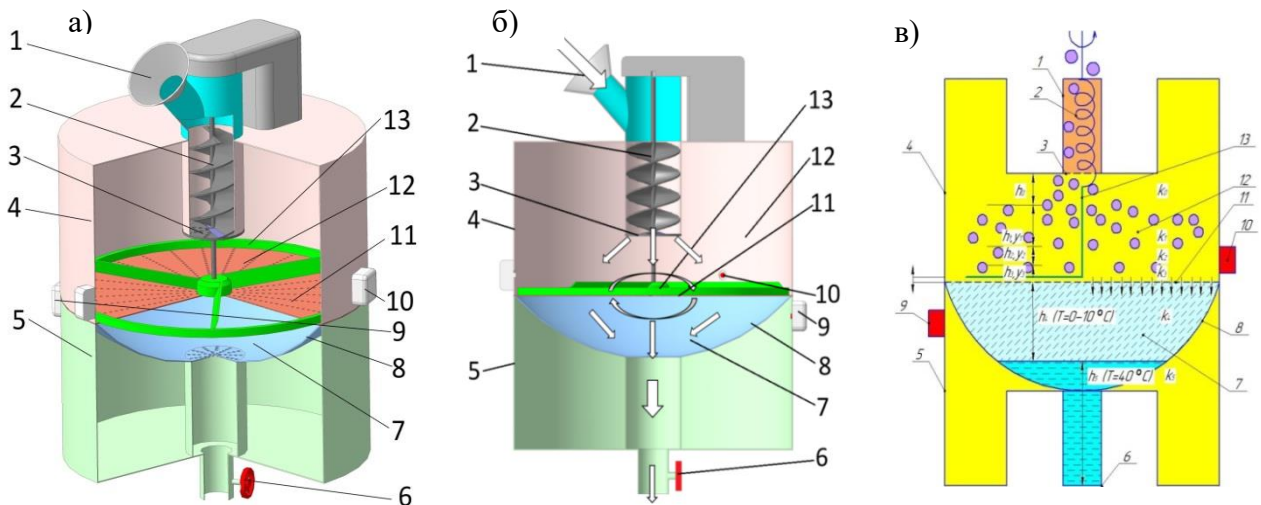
СВЧ установка с тороидальными резонаторами: а) общий вид; б) схематическое изображение; в) схема процесса; 1 – загрузочное устройство, 2 – нагнетательный шнек, 3 – нож с решеткой; 4 – верхний резонатор; 5 – нижний резонатор; 6 – шаровый кран; 7 – конденсаторная часть нижнего резонатора; 8 – диэлектрическая тарелка без дна; 9 – магнетроны на нижнем резонаторе; 10 – магнетроны на верхнем резонаторе; 11 – общее перфорированное основание резонаторов; 12 – конденсаторная часть верхнего резонатора; 13 – диэлектрический перемешивающий механизм
